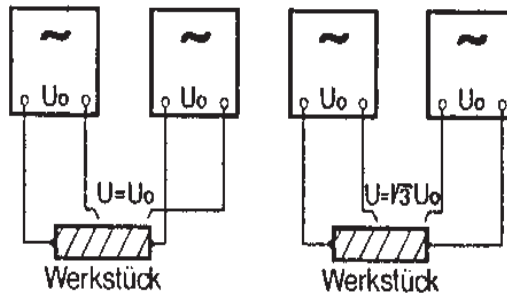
Die zum Schweißen gewählte Polung ist schweißtechnisch bedingt.
